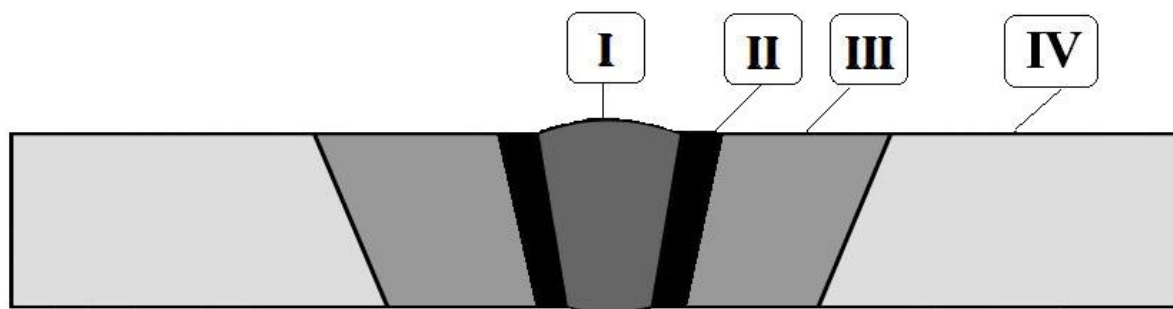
Ділянки зварного з'єднання (за даними праці [15]) : ділянка I – зварний шов; ділянка II – межа зварного шва – зона термічного впливу; ділянка III – зона термічного впливу; ділянка IV – межа зони термічного впливу – основний метал [12–16]
